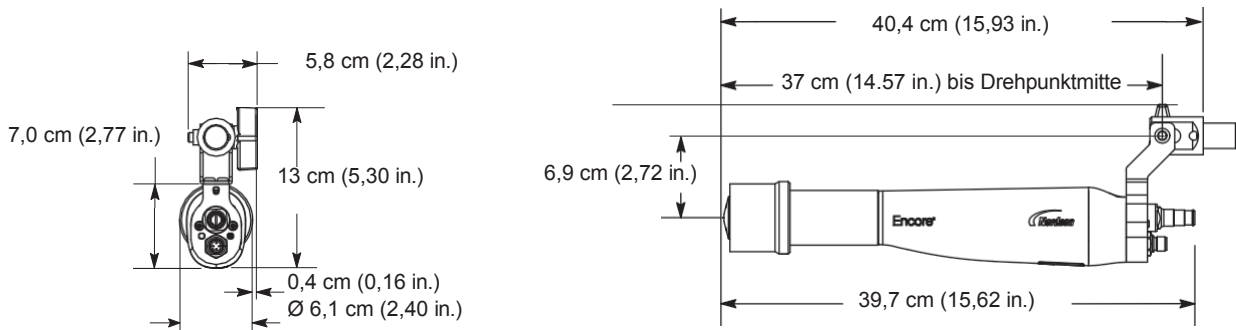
Abmessungen und Gewichte der Pistole (mit konischer Düse)
